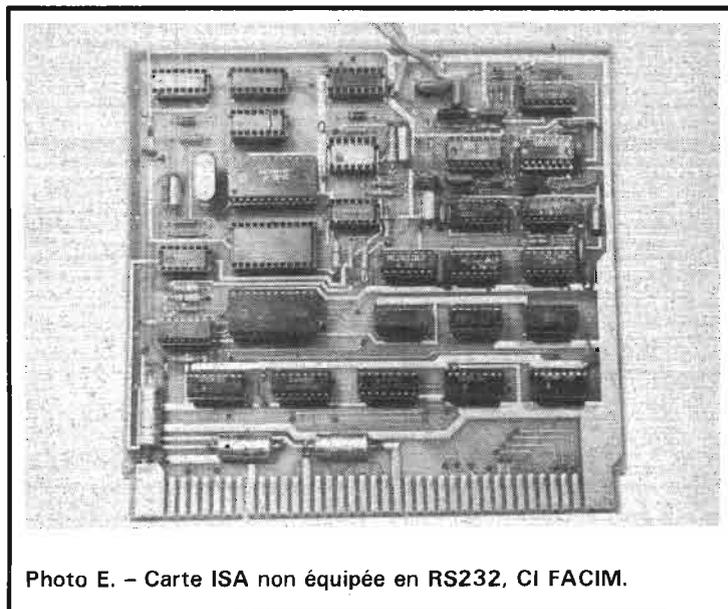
Photo E. - Carte ISA non équipée en RS232, CI FACIM.
